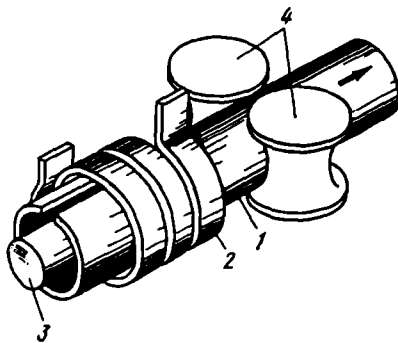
Схема процесса индукционной сварки труб:
